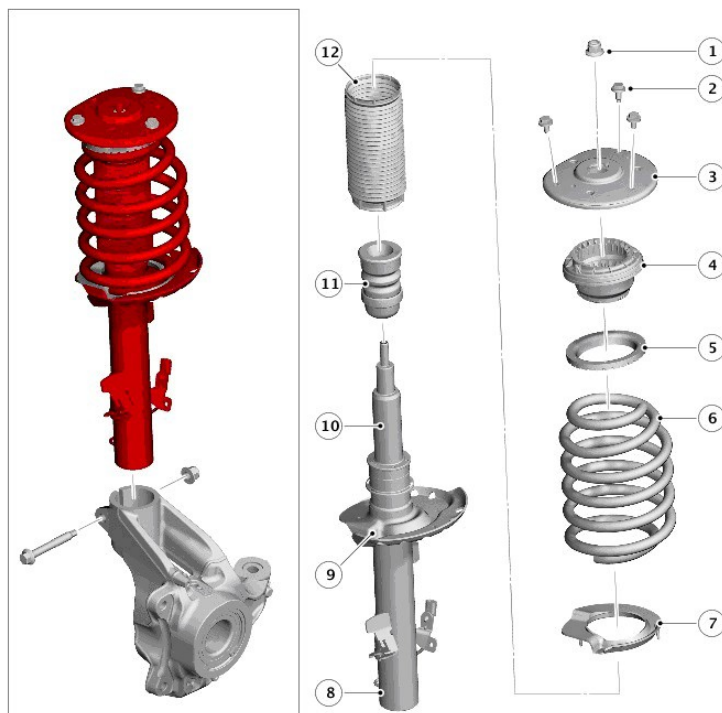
Пружина и амортизатор адаптивной динамической системы передней подвески Discovery Sport (стандартный амортизатор аналогичный)
